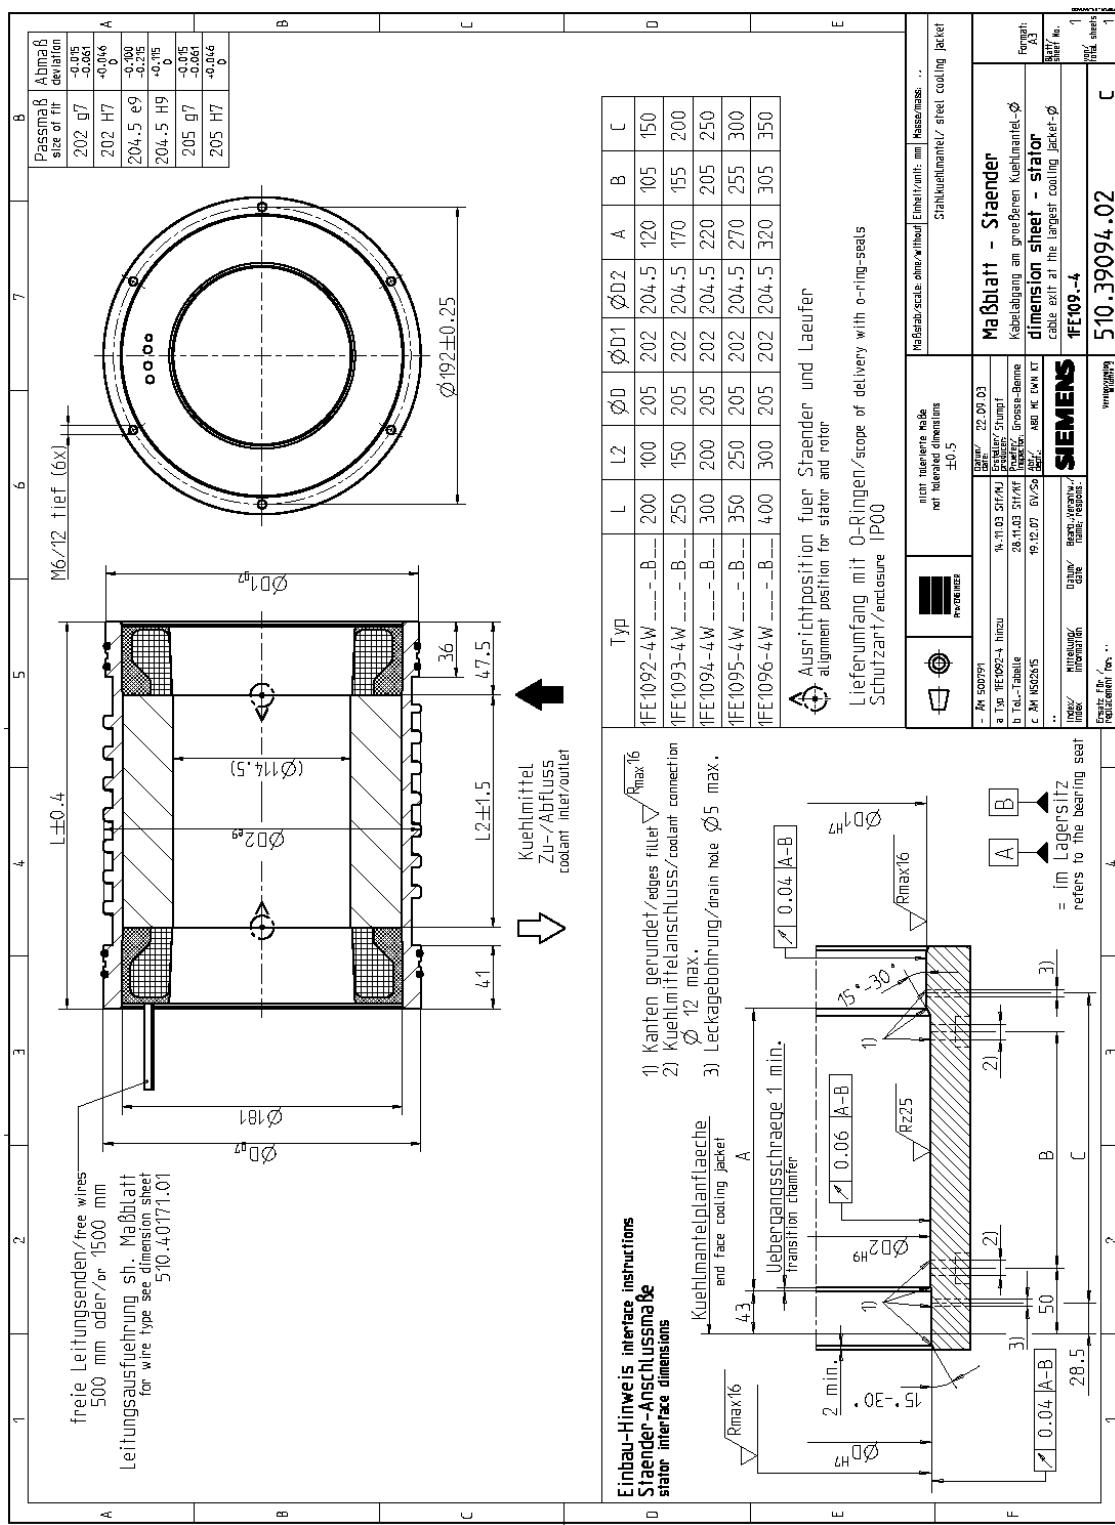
1FE109□-4, Ständer mit Kühlmantel, Kabelabgang am größeren Kühlmanteldurchmesser
